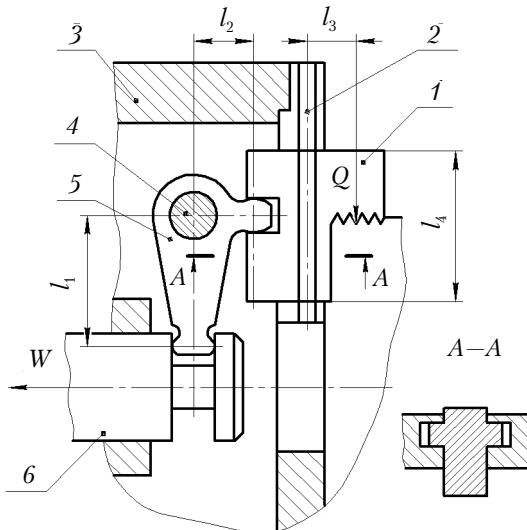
Схема рычажного самоцентрирующего патрона
